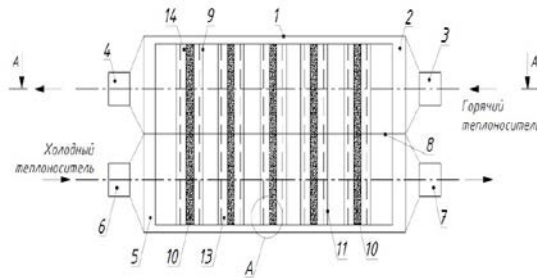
Общий вид КМТ: 1 – корпус; 2 – камера охлаждения; 3 – патрубок горячего теплоносителя; 4 – патрубок холодного теплоносителя; 5 – камера нагрева; 6 – патрубок входа; 7 – патрубок выхода; 8 – перегородка; 9 – тепловые трубы; 10 – подъемный фитиль; 11 – решетка; 12 – ячейки; 13 – зона испарения; 14 – зона конденсации.
